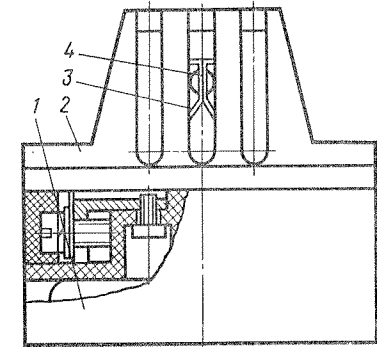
Пожарный локомотивный извещатель ИПЛ:
